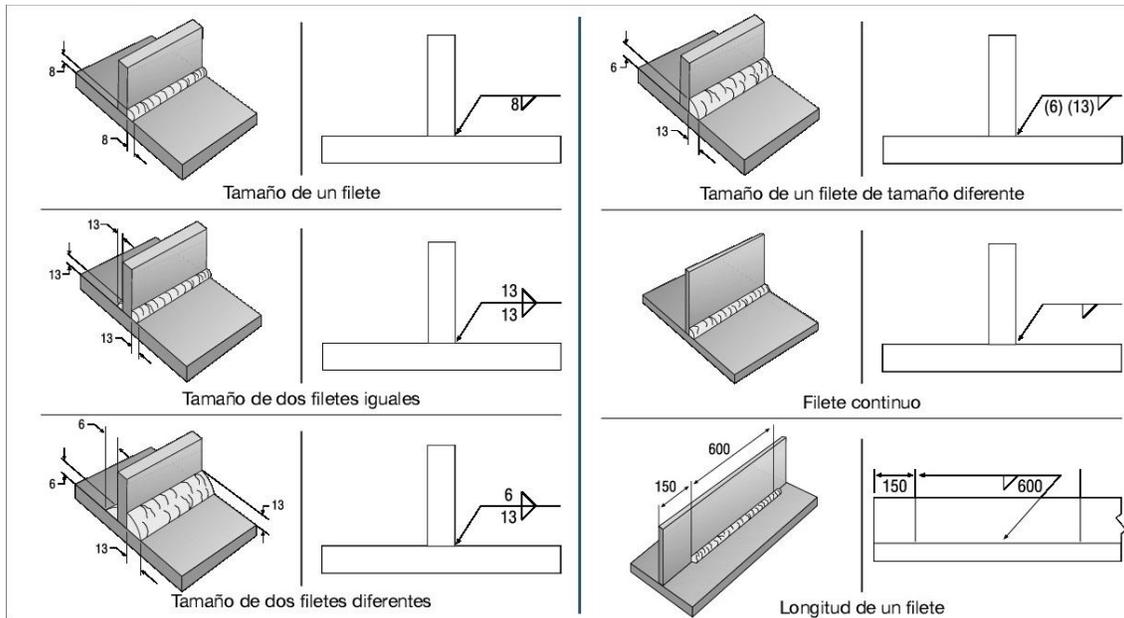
Ejemplos de simbología para soldadura de filete.
